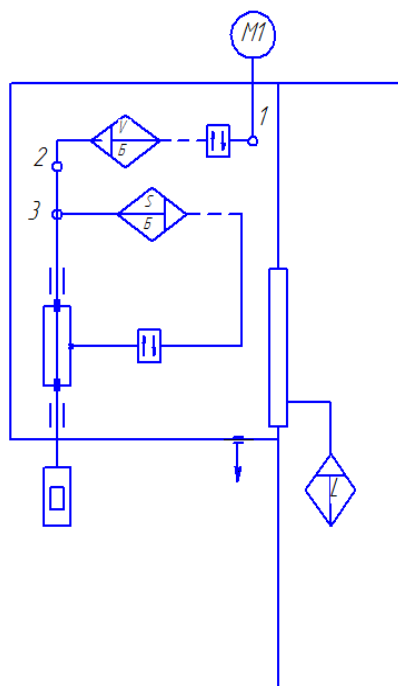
Кінематичний ланцюг переміщення свердлильної головки
